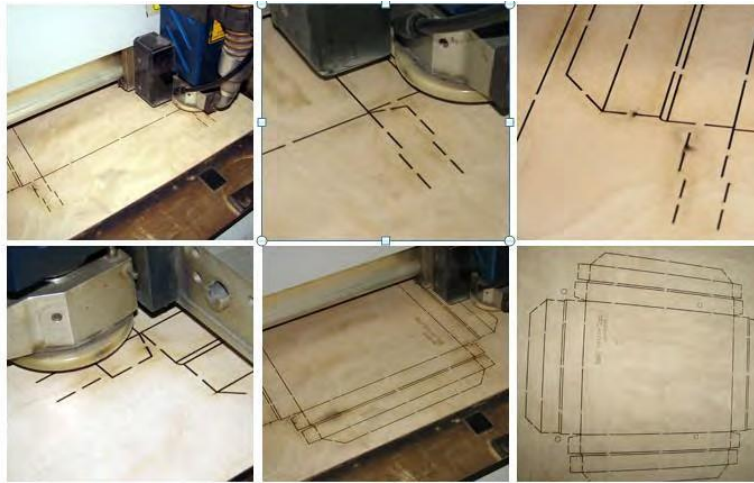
Виготовлення фанерної основи для штанцформи
